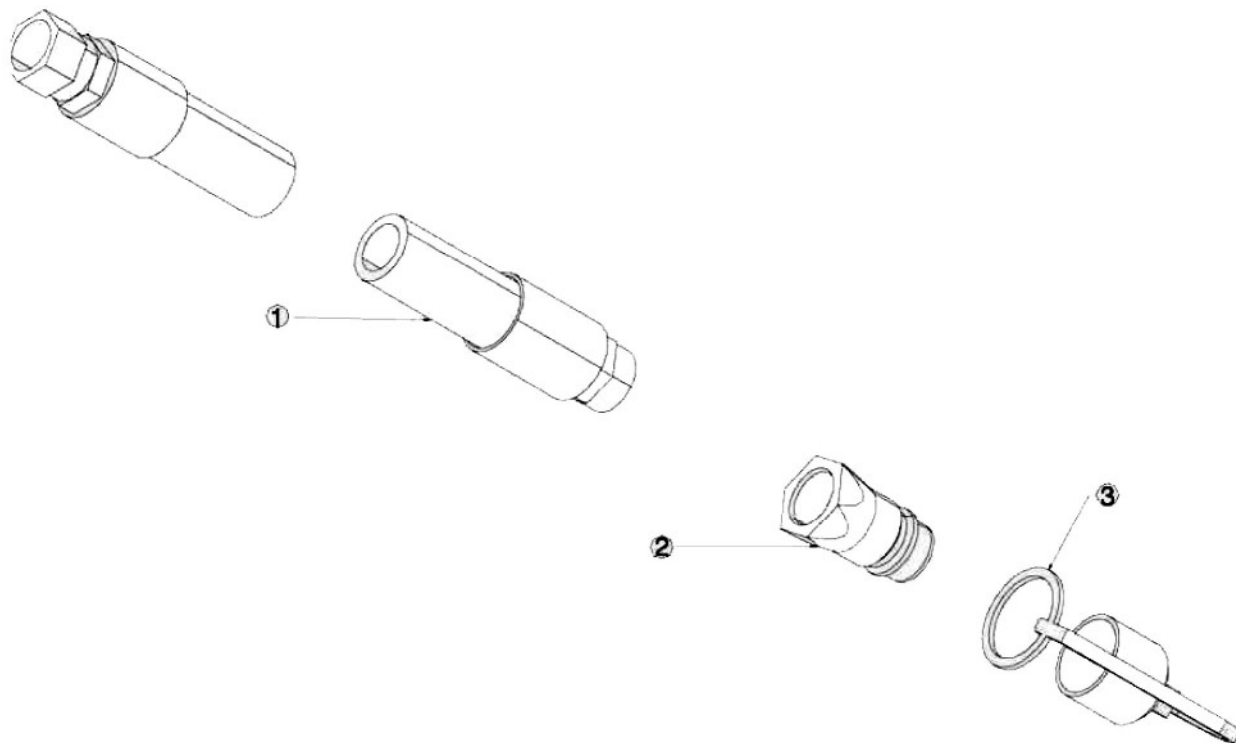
Чертеж 3/8 линии гидроцилиндров - А8013-00
